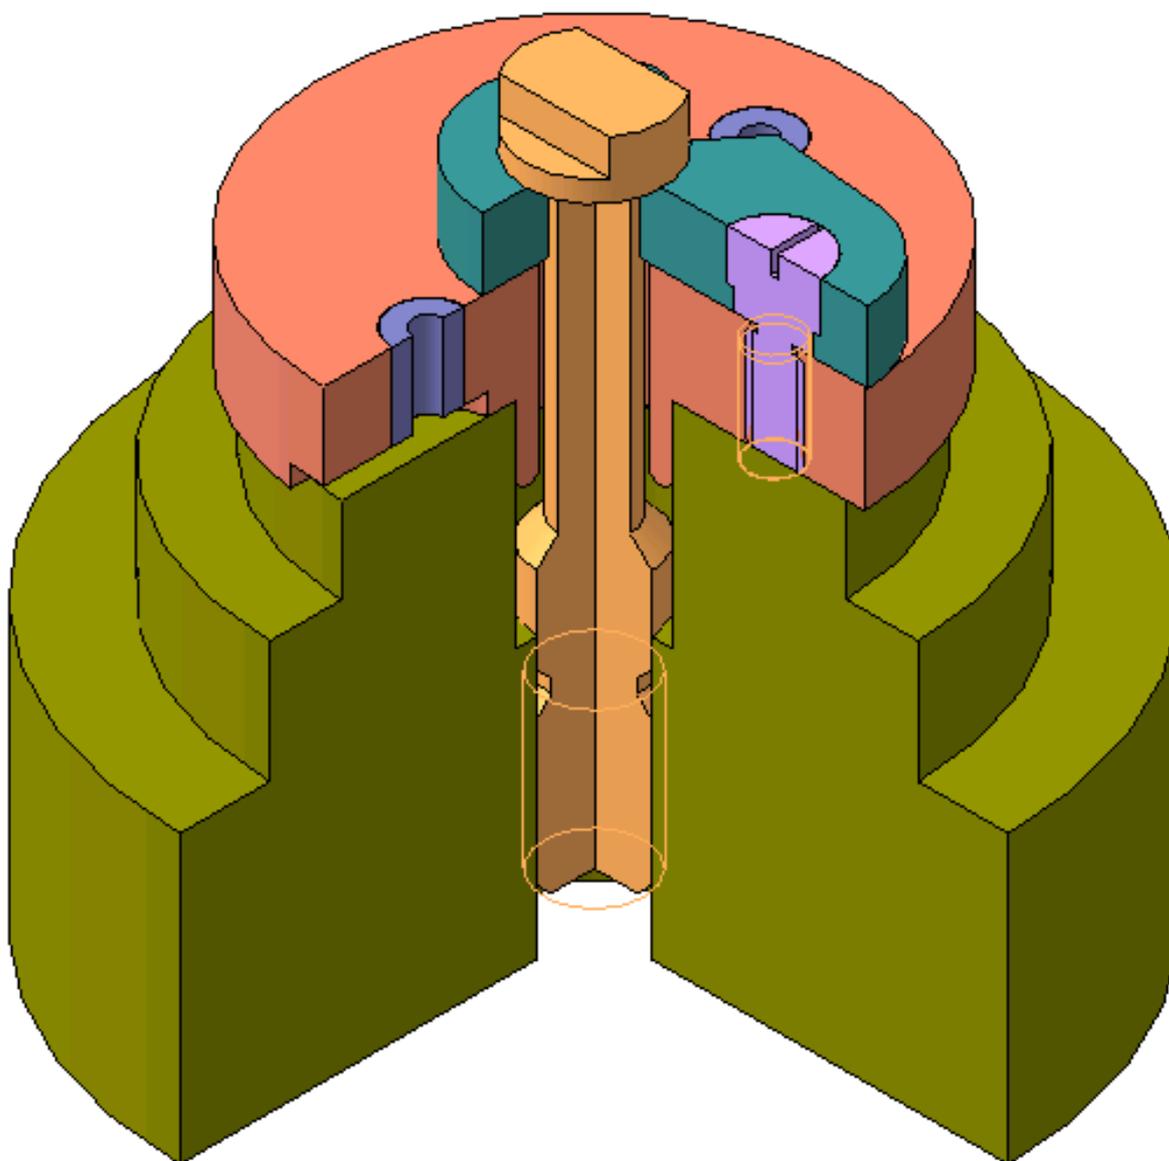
3D-модель сборки изделия «Кондуктор-1» (варианты 3, 23)
